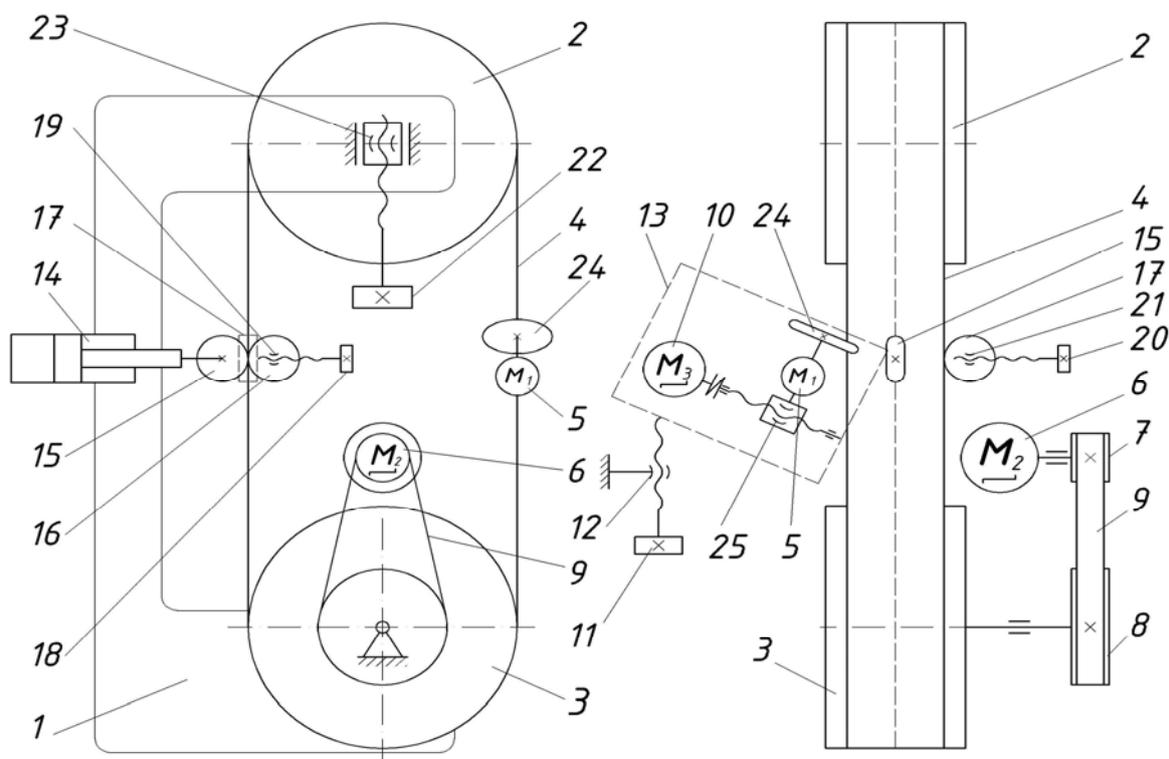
Схема комбинированного станка для подготовки ленточных пил
